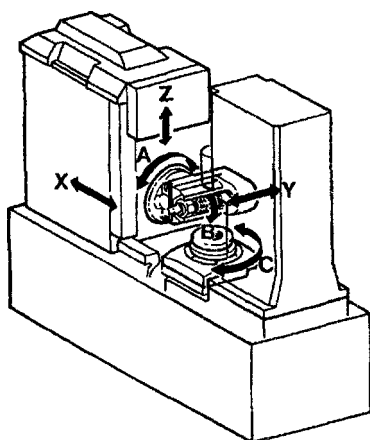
Типовая компоновка зубофрезерного полуавтомата
